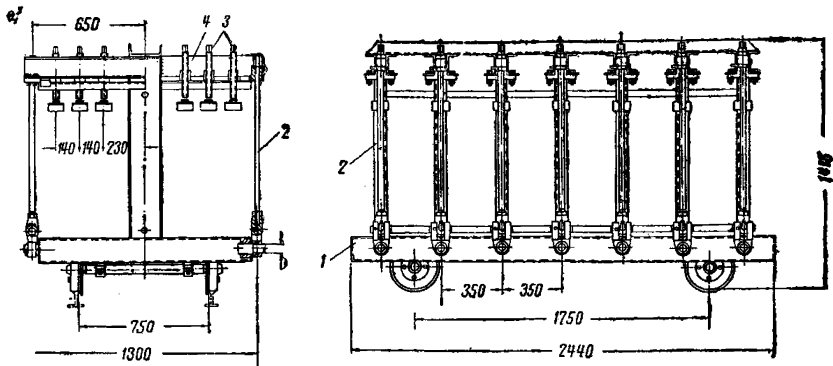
Прессвагонетка для запрессовки склеиваемых деталей:
